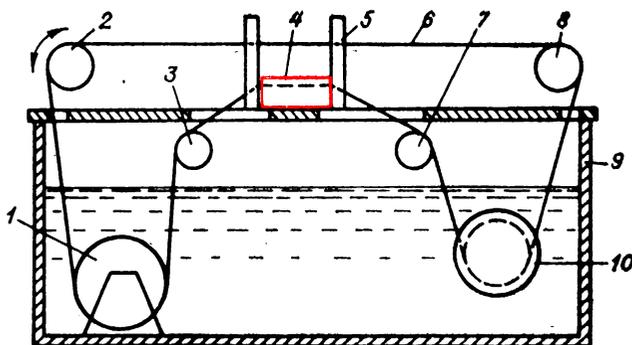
Схема станка для резки кристаллов мокрой нитью.
